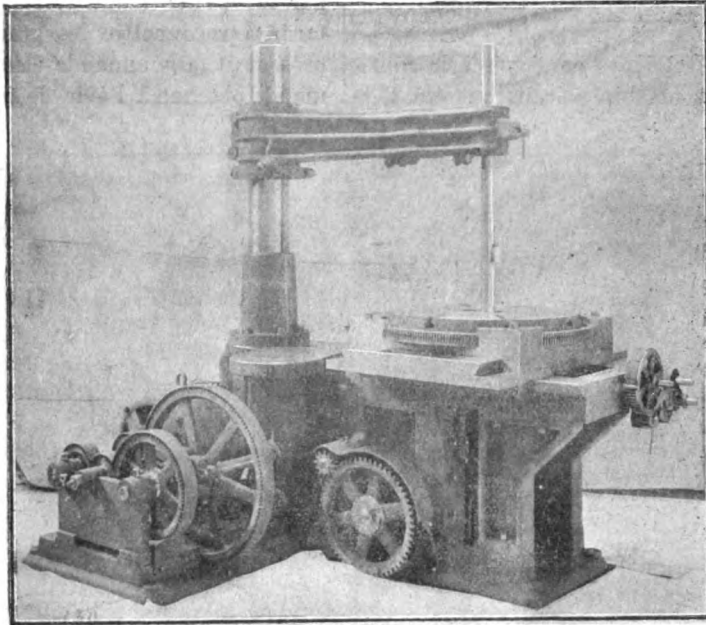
Machine à fraiser de MM. Baker frères, commandée par un moteur électrique Bullock.
